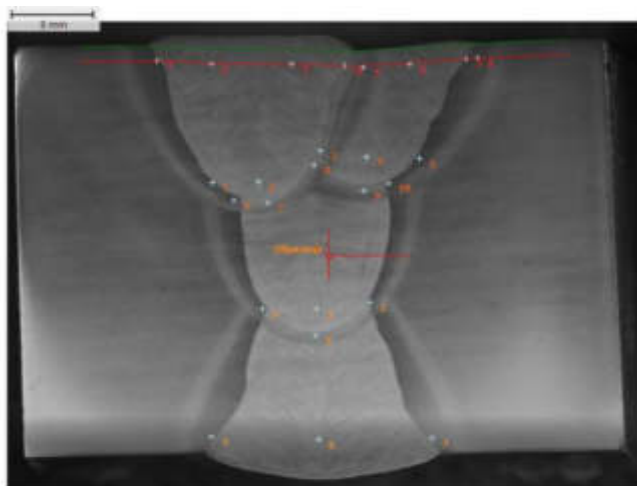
Шлиф после сварки с применением четырех дуг
